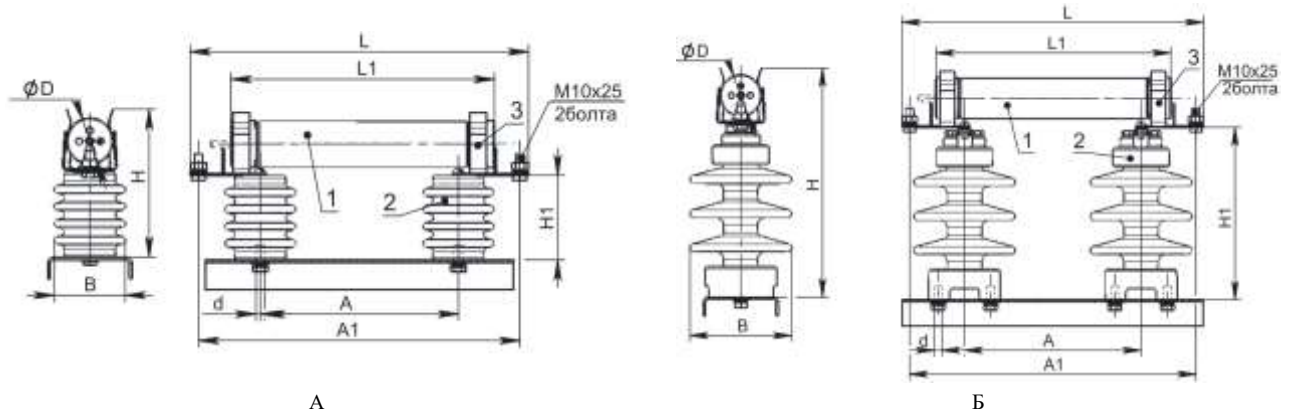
Габаритные и установочные размеры предохранителей ПКТ-101, ПКТ-102.
